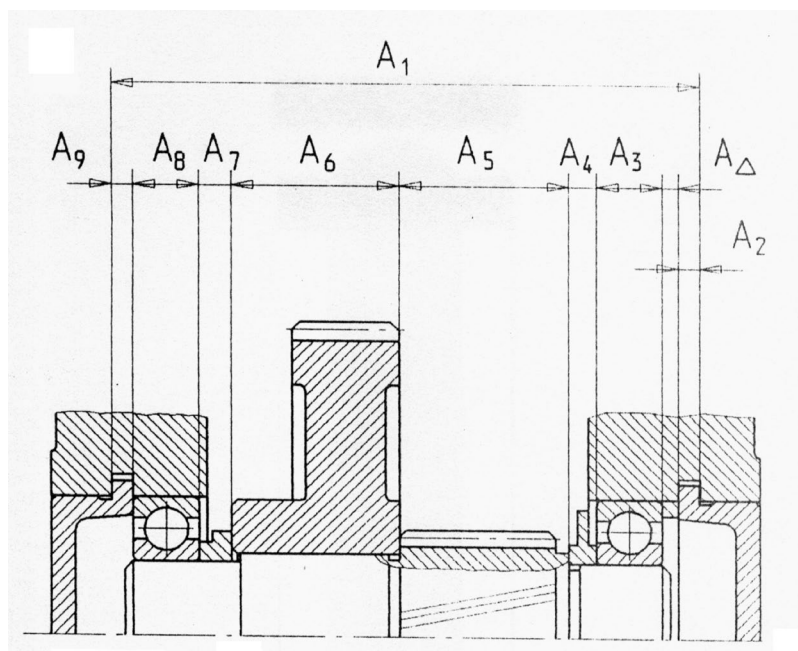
Сборочный чертеж узла и его размерная цепь
